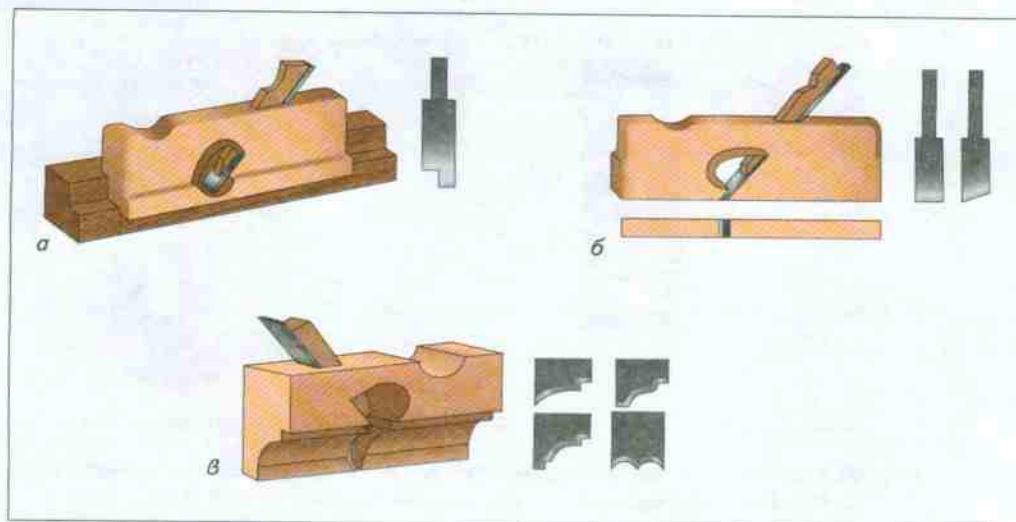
Струги и ножи для выборки профилей брусков: а — фальцгебель, б — зензубель (дан вид снизу), в — калёвка
